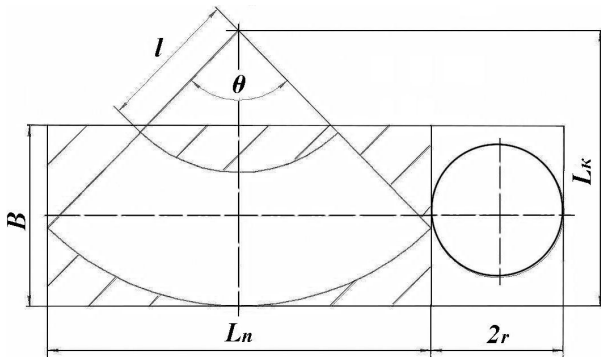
Форма заготовки для изготовления конического полуфабриката
